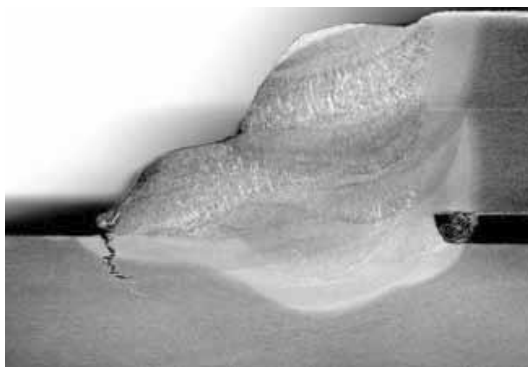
Образование на участке перехода от внешнего сварного шва
